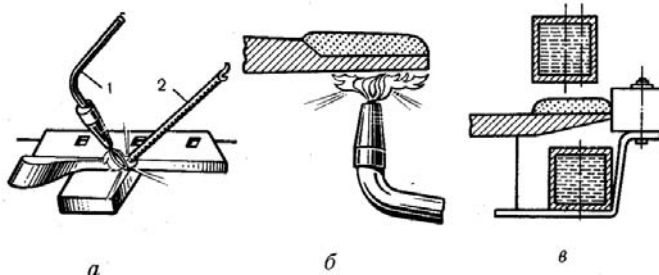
Способы нагрева лезвия плужного лемеха при наплавке твердого сплава: а — прямой нагрев прутка из твердого сплава «Сормайт-1» газовой горелкой; б — нижний нагрев лезвия с насыпной шихтой; в — нагрев токами высокой частоты; 1 — горелка; 2 — пруток из твердого сплава
